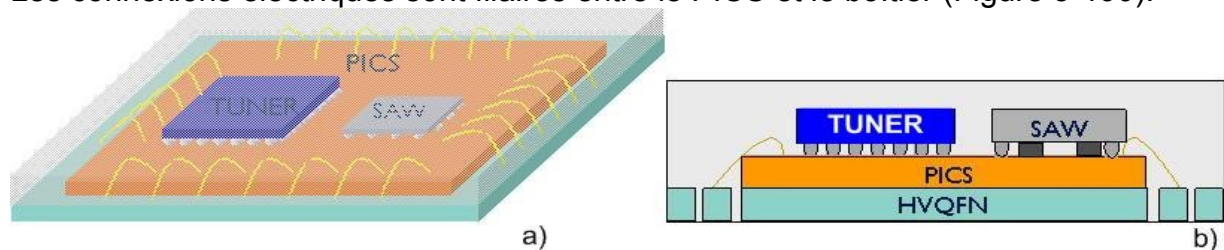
Schéma de l'assemblage complet dans un boîtier de type HVQFN vue de dessus (a) et vue en coupe (b).
